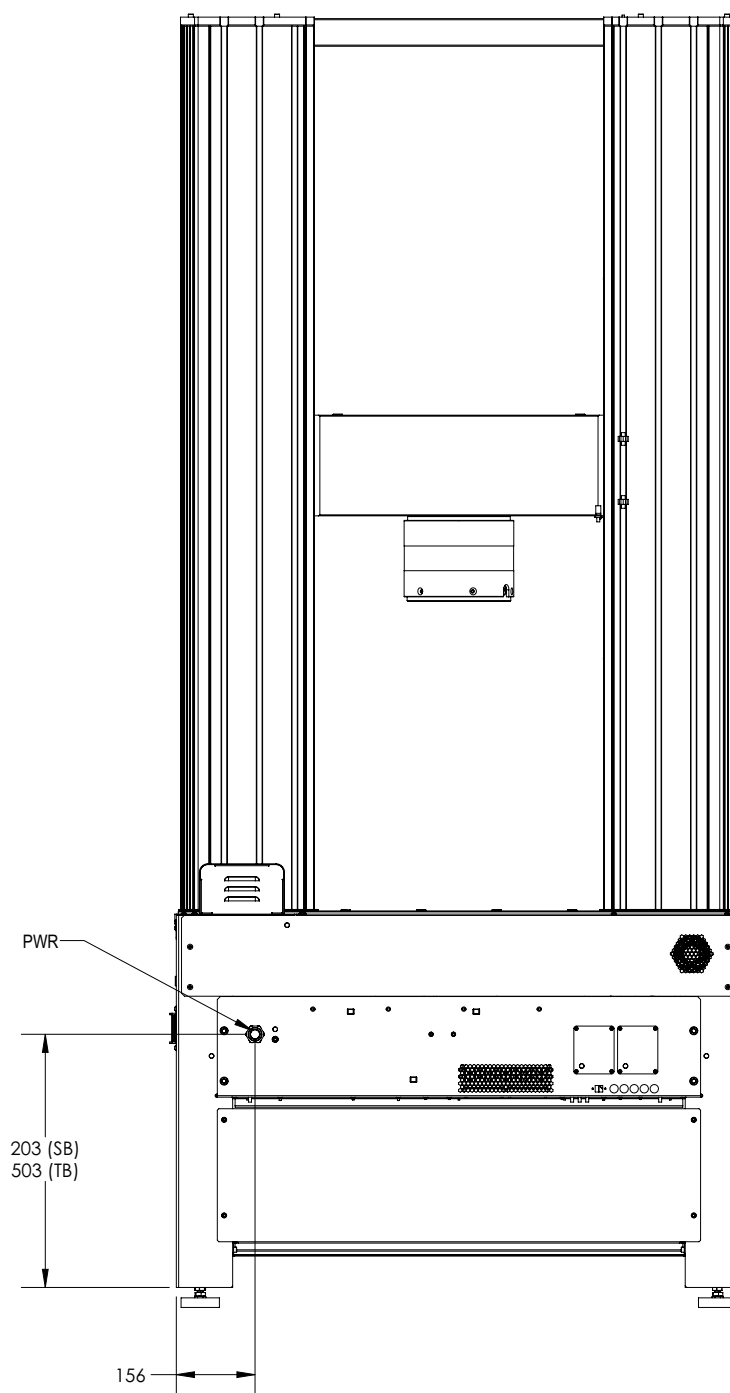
68FM-300 dimensions du bâti – vue de dos
